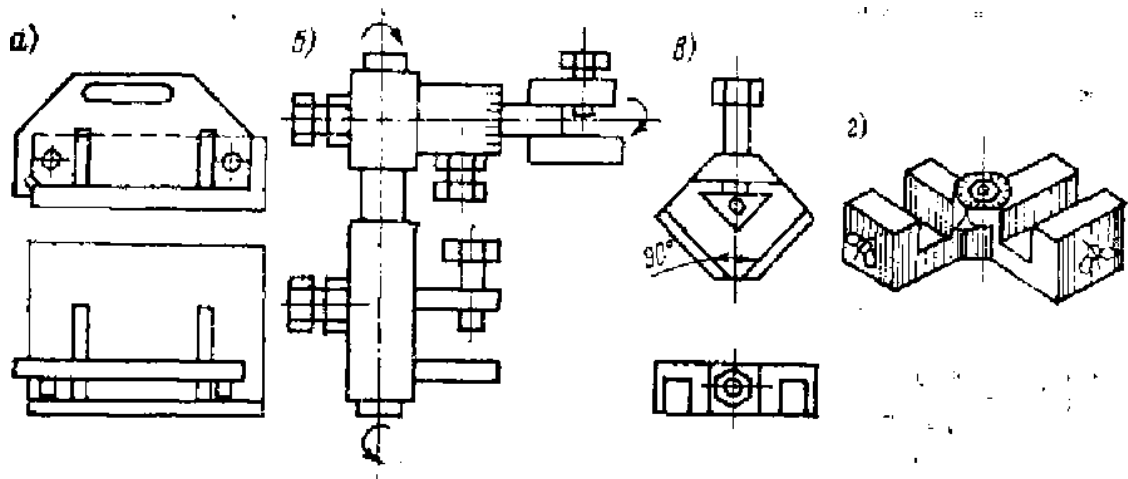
Специализированные сборочные приспособления а – шаблоны; б – переносное поворотное приспособление; в – для сборки деталей под углом 90° ; з – для сборки деталей под различными углами
